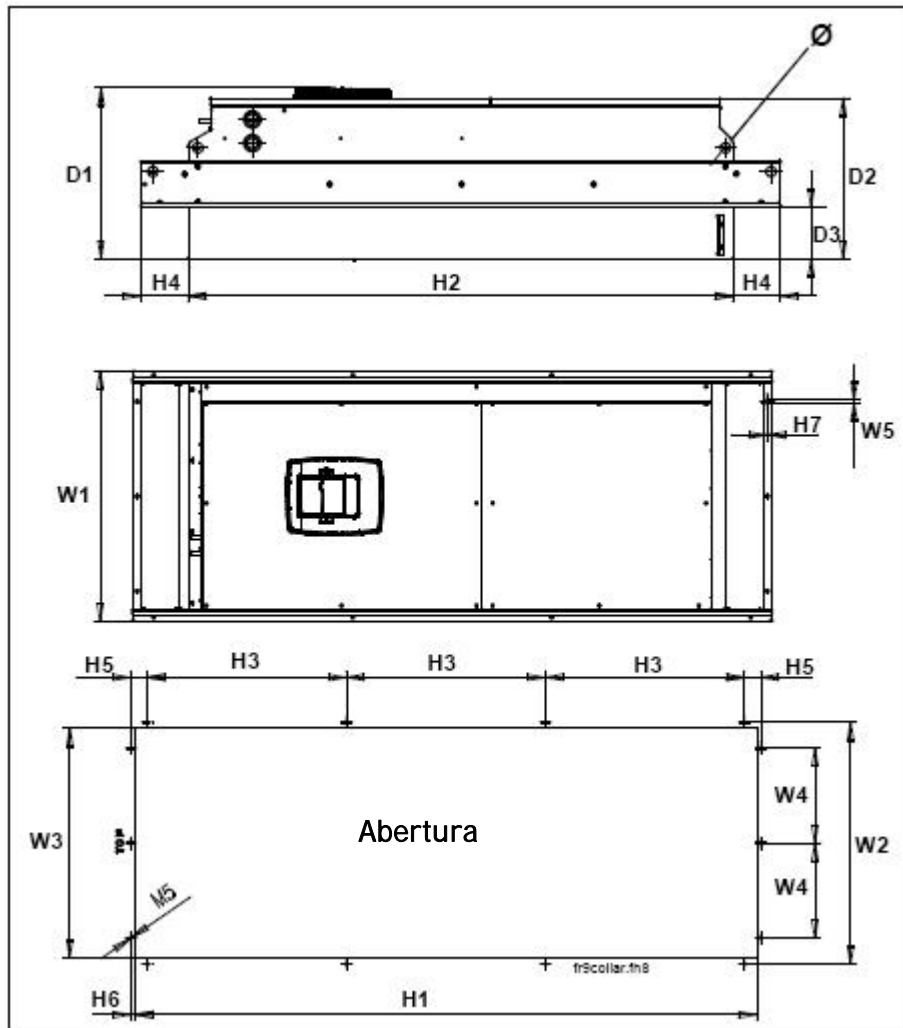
Dimensões do Vacon NX_ . FR9 montagem por flange
